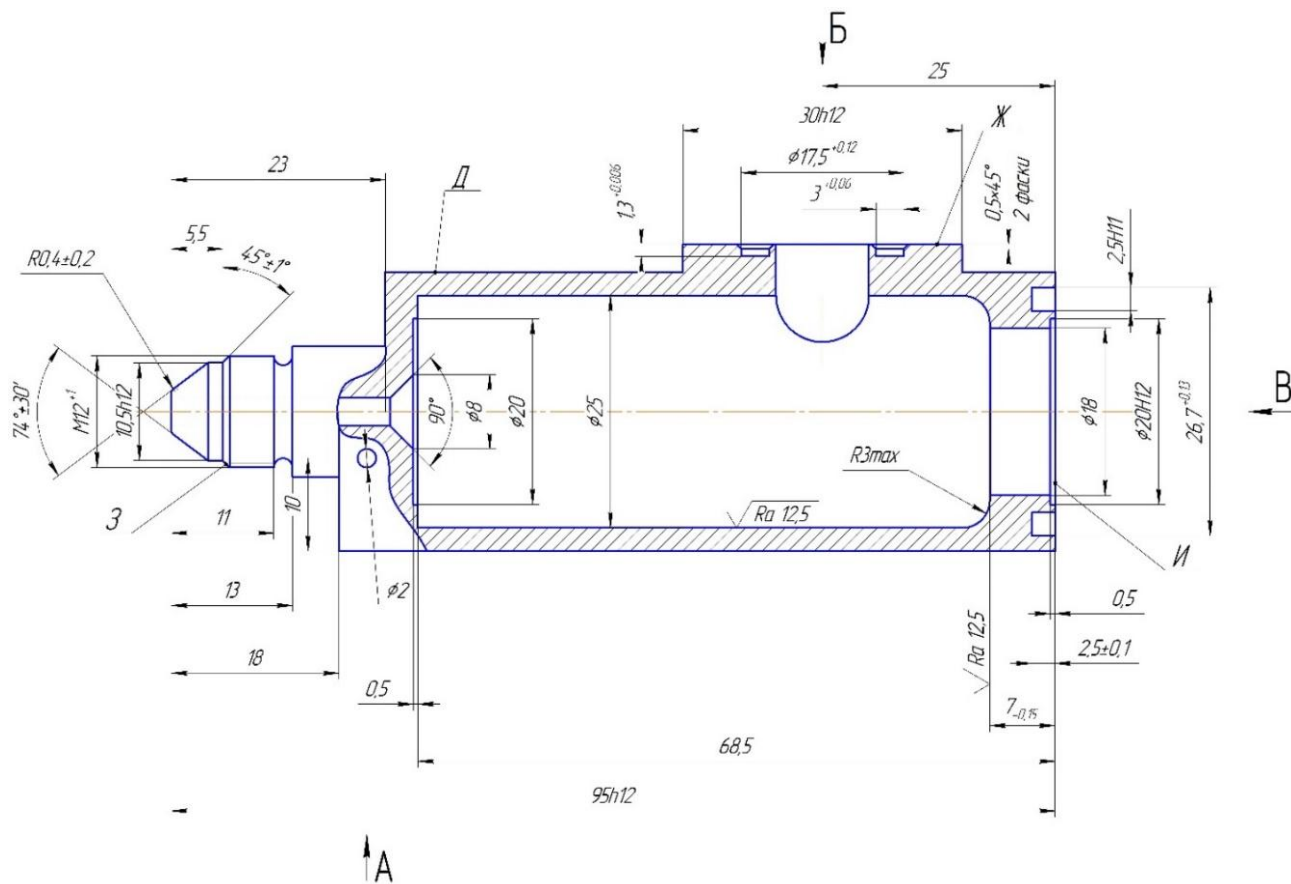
Деталь «Корпус влагопоглатителя»
